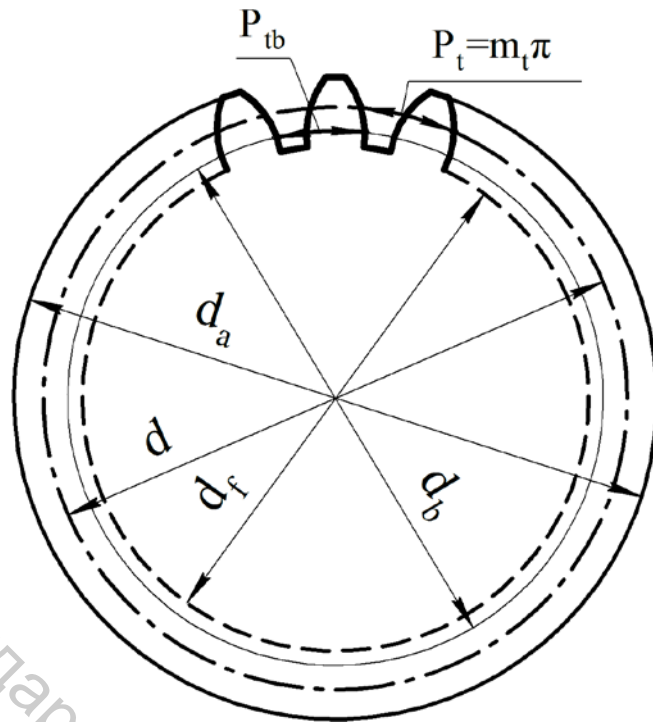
Эвольвентное цилиндрическое колесо: диаметры и шаги зацепления (7.8)
